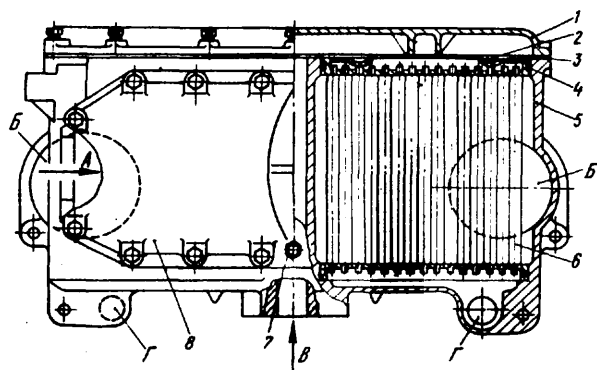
Охладитель наддувочного воздуха («вода — воздух»): 1 — крышка; 2 — защитная сетка; 3 — прокладки; 4 — уплотнительные кольца; 5 — корпус; 6 — охлаждающий элемент; 7 — пробка; 8 — задняя крышка; А — подвод воздуха от турбокомпрессора; Б — выход охлаждаемого воздуха во впускные трубопроводы; В — подвод охлаждающей жидкости; Г — отвод охлаждающей жидкости в водяные трубы
